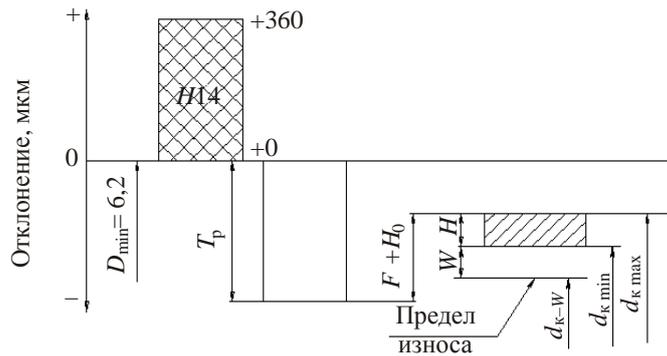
Схема расположения полей допусков калибров для отверстий $\varnothing 6,2$ мм:
